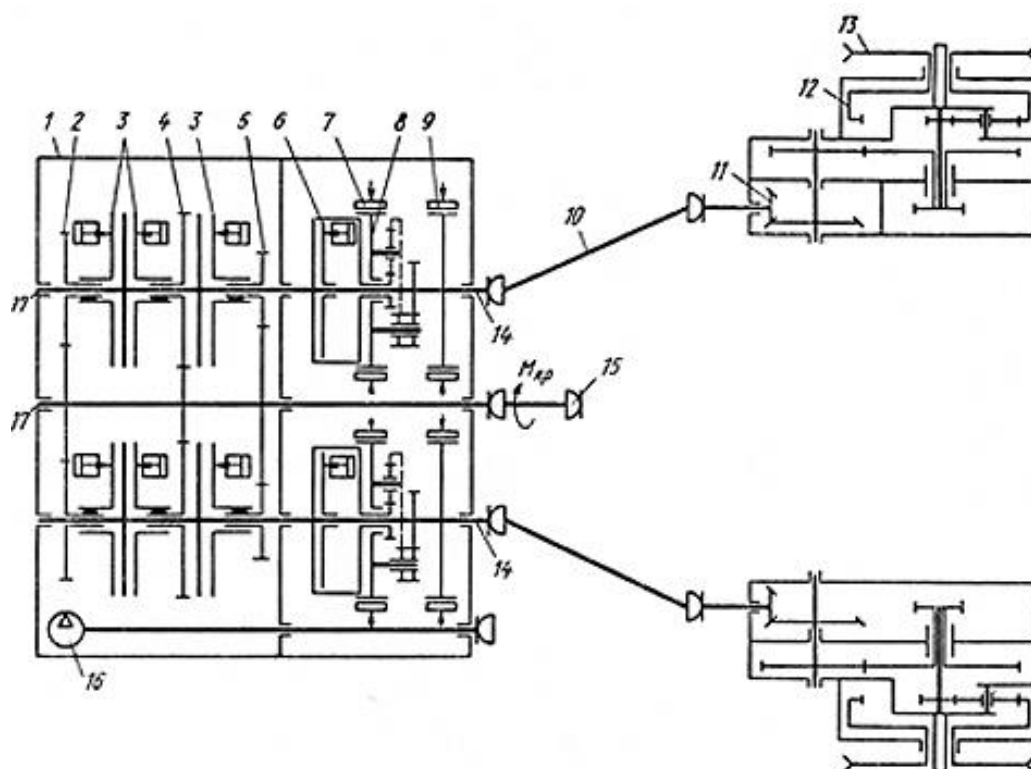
Ступенчатый механизм поворота (поворот бортовыми КПП)
